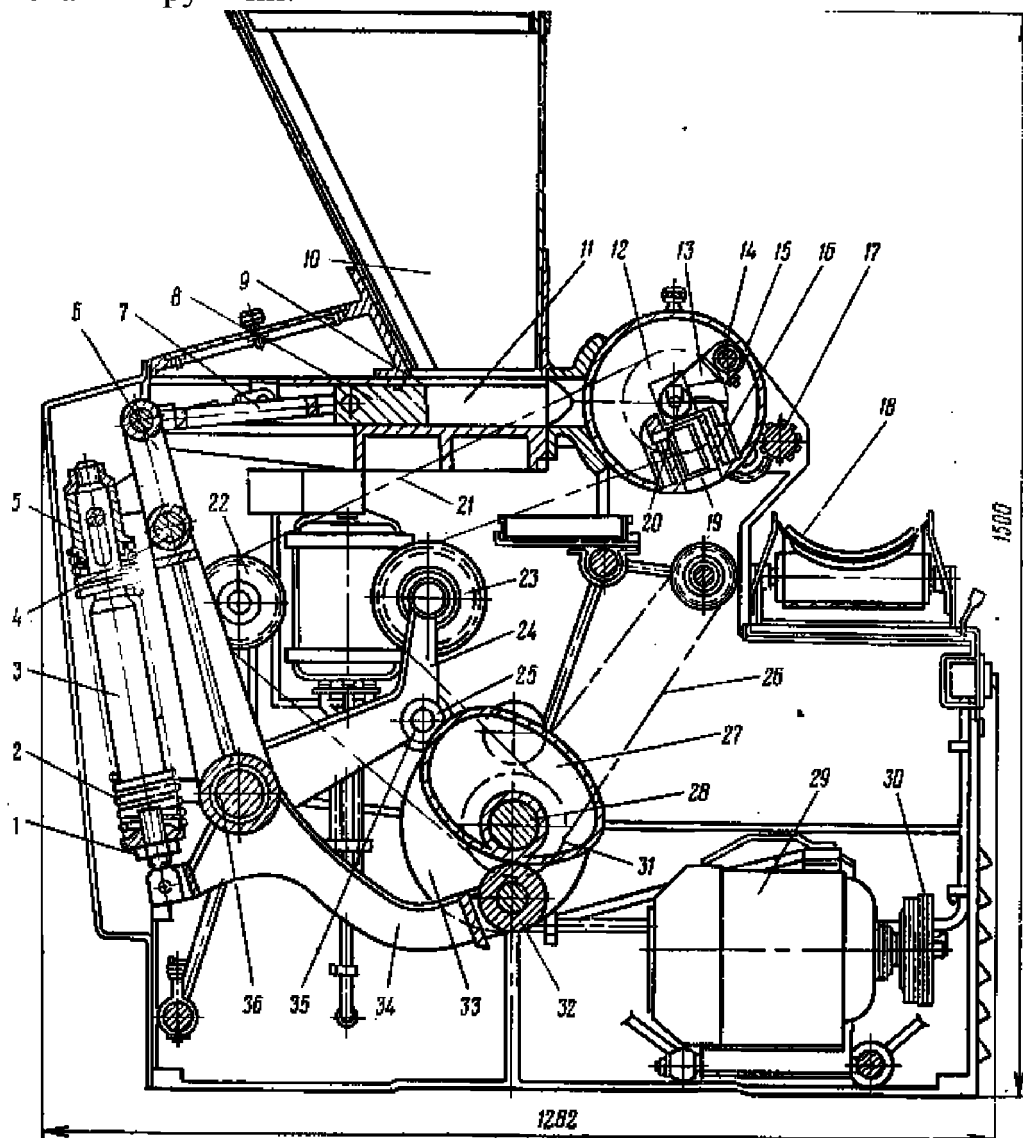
Тістоподільна машина РМК: 1 – регулювальна гайка; 2 – пружина; 3 – качалка; 4 – шарнір; 5 – обойма; 6 – ричаг; 7 – тяга; 8 – нагнітальний поршень; 9 – заслінка; 10 – приймальна воронка; 11 – тістова камера; 12, 22, 23, 31 – зірочки; 13 – ричажки; 14 – валок; 15 – подільна головка; 16 – мірний поршень; 17 – рифлений валок; 18 – стрічковий транспортер; 19 – мірні кармани; 20 – ролики; 21 – ланцюгова передача; 24 – ричаг; 25 – ролик; 26 – ланцюгова передача; 27 – кулачок; 28 – головний вал; 29 – електродвигун; 30 – клинопасова передача; 32 – ролик; 33 – кулачок; 34 – ричаг; 35, 36 – вісь
